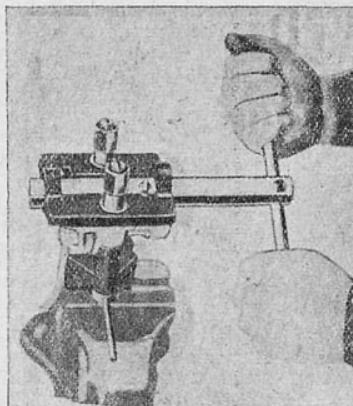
Процесс нарезки смазочных канавок крышки коренного подшипника
